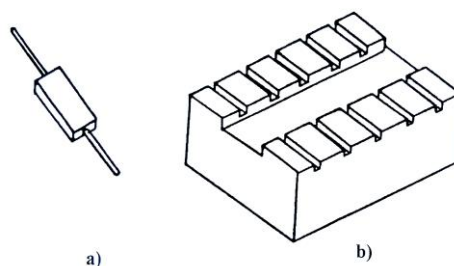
формы образцов (а), и приспособление с канавкой (b) для расположения образцов.
